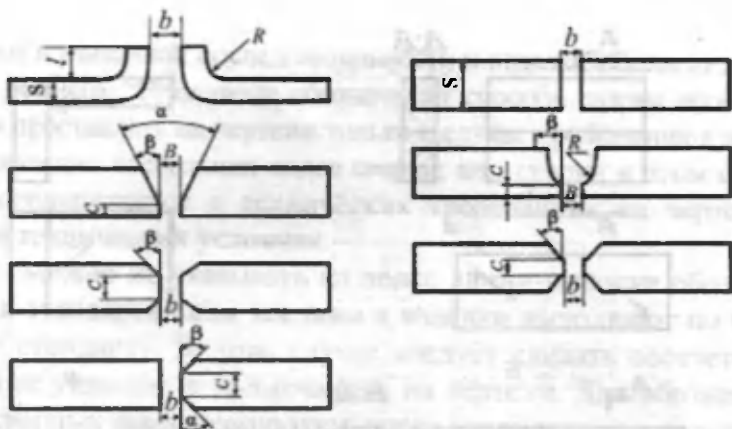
Примеры подготовки кромок для сварки в стыковых соединениях
